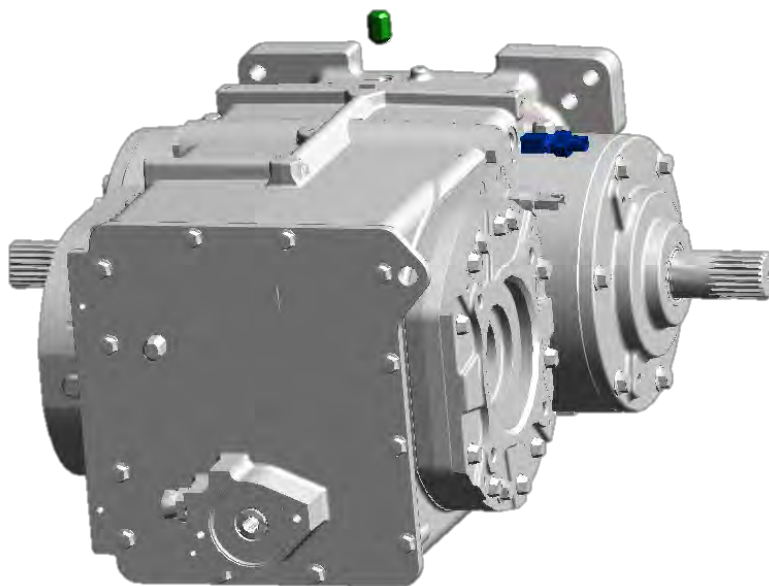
“Explosionado del proceso de montaje de la estación 5”
